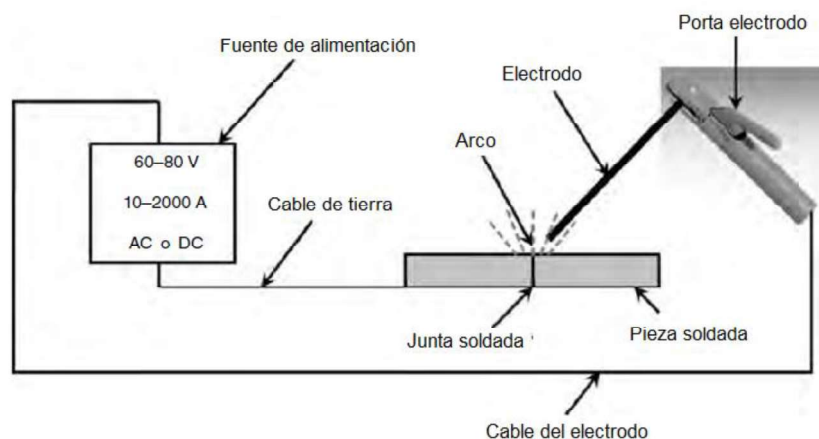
Circuito de soldadura por arco (representación SMAW).
